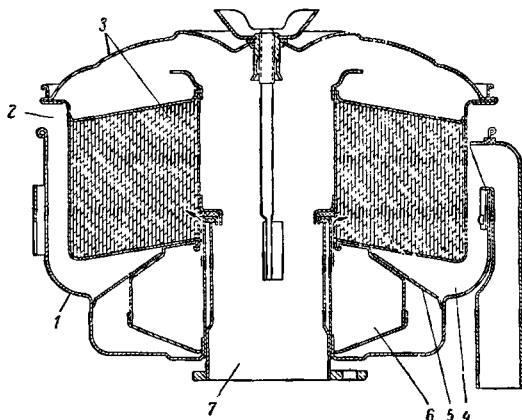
Воздушный фильтр карбюратора двигателя ЗИЛ-120.
